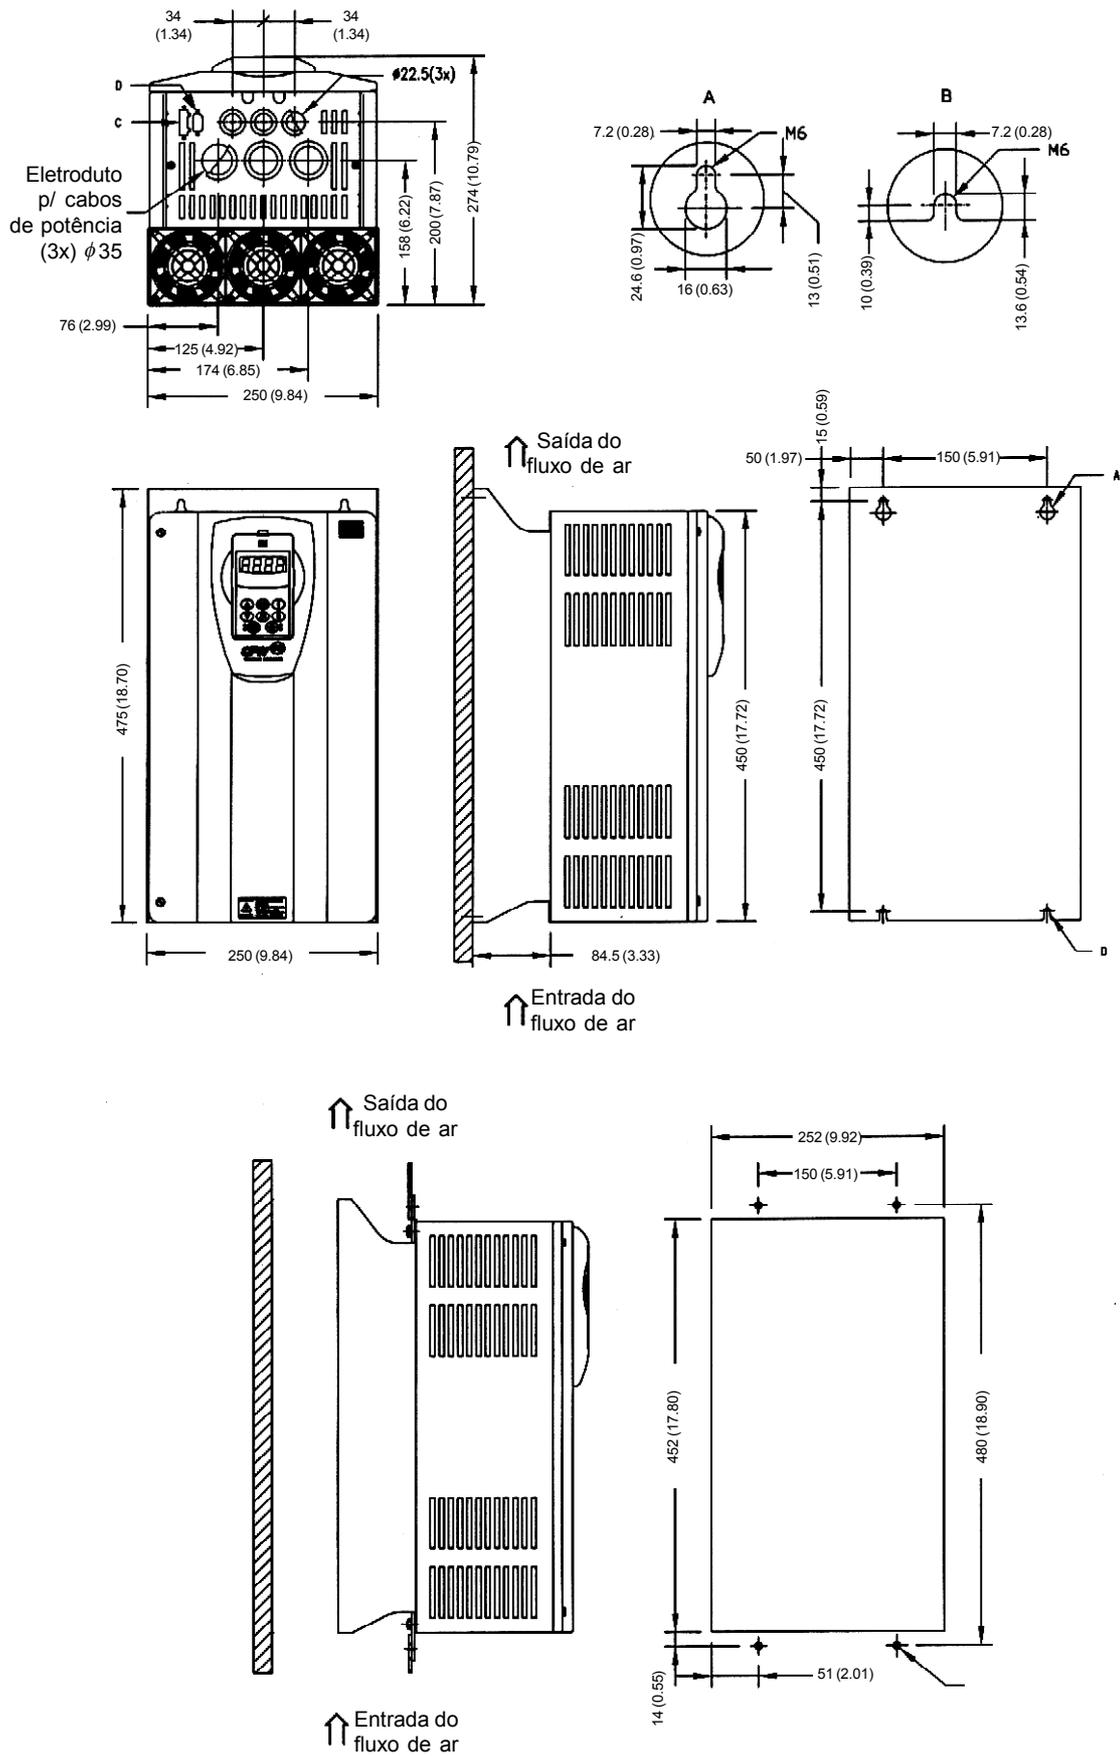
Mecânica 4 - Dimensões em mm (polegadas)
